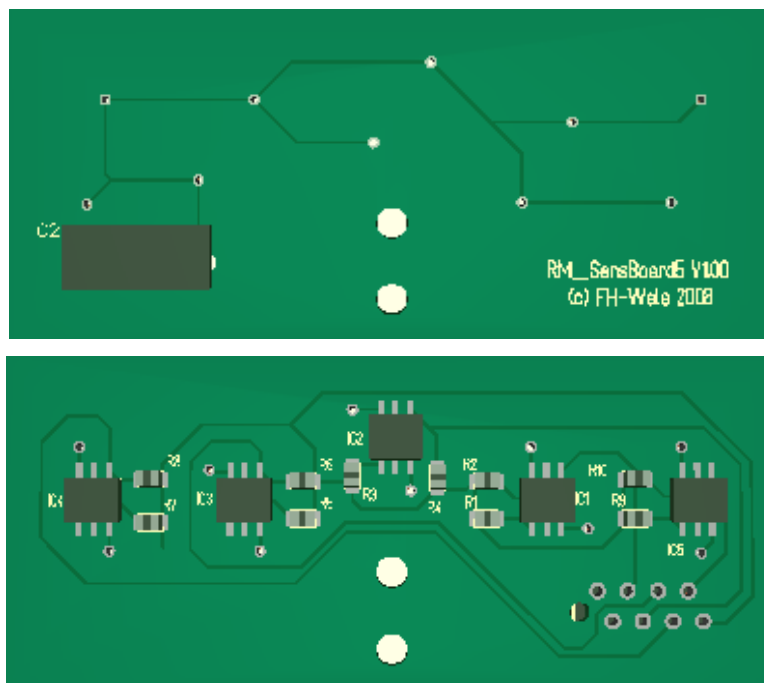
Linienboard 5Sensor - 3D-Ansicht - Top & Bottom
